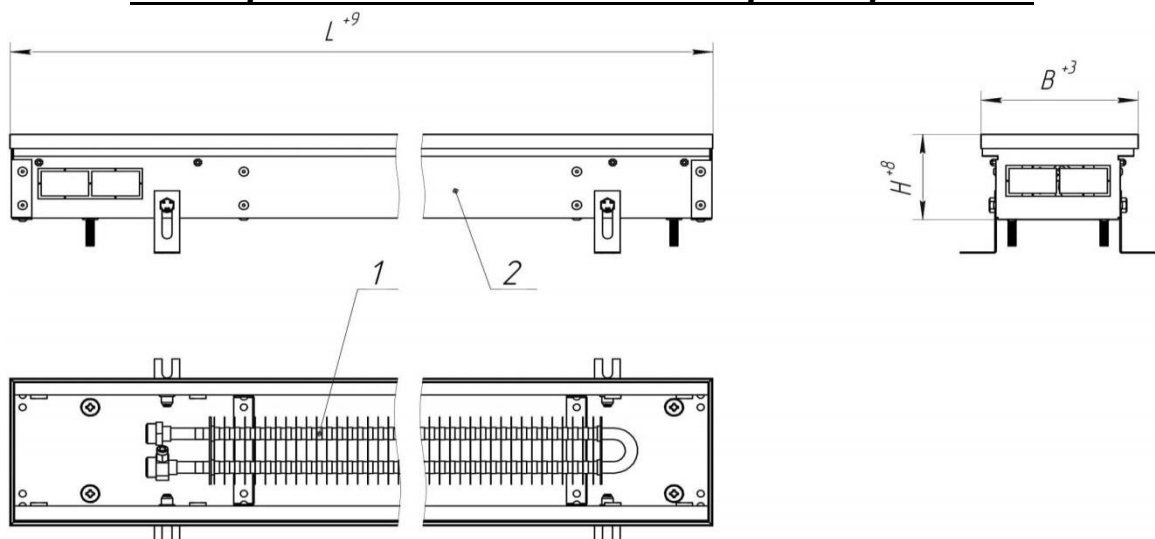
Общий вид конвектора Techno Power без решетки.
